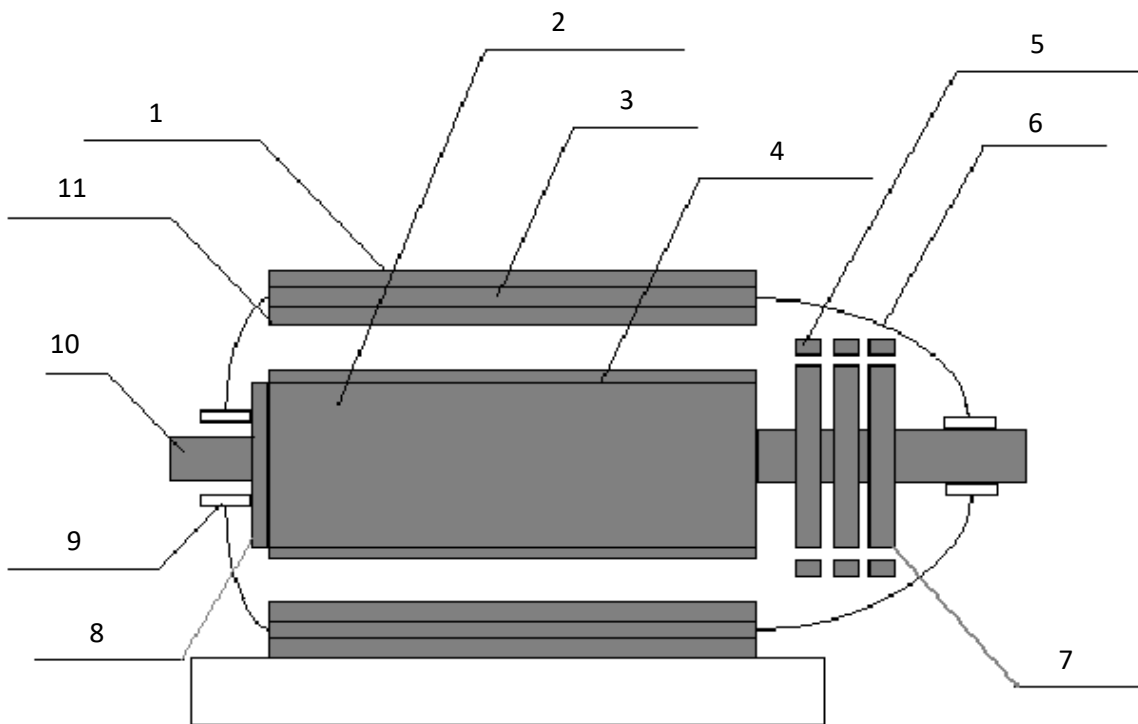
Конструкция асинхронного двигателя: 1-станина; 2-сердечник ротора; 3 - сердечник статора; 4 – обмотка ротора; 5 – щеточный аппарат; 6 – подшипниковые щиты; 7 – контактные кольца; 8 – крыльчатка вентилятора; 9 – подшипники; 10 – вал; 11- обмотка статора.
